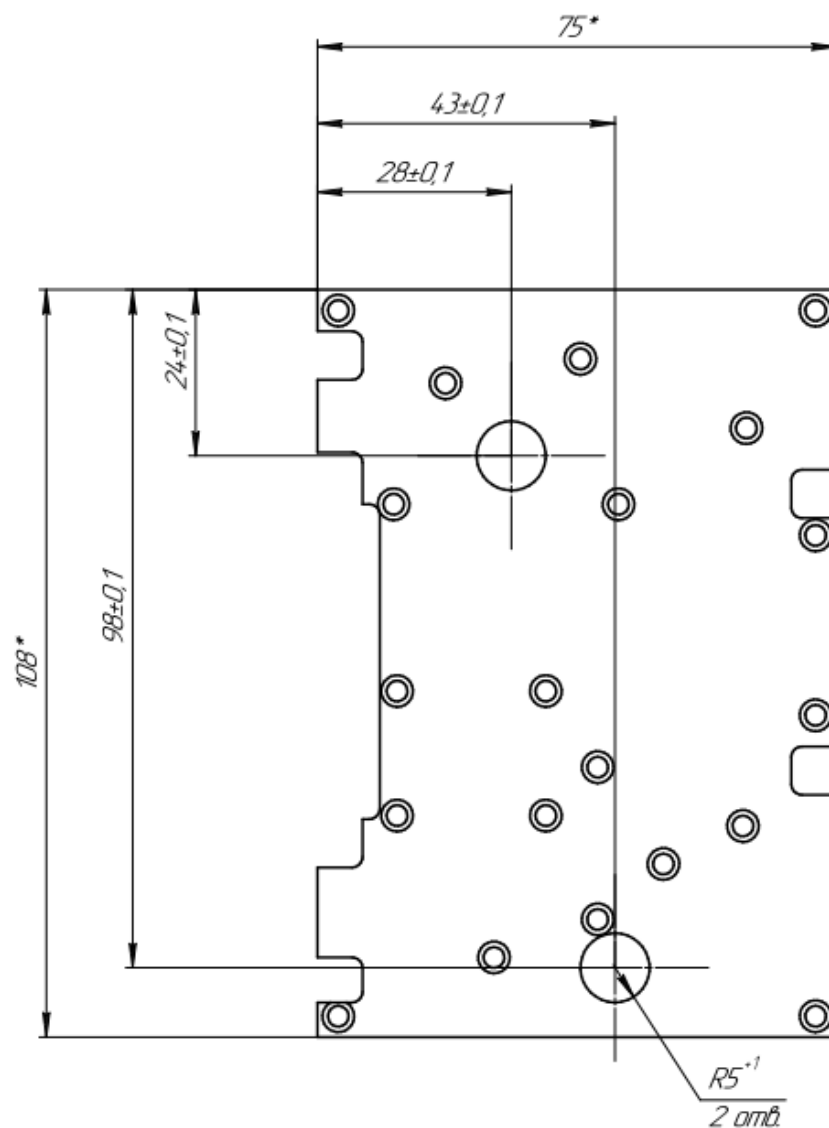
Эскиз крышки ЖНКЮ.741424.703 с отверстиями для настройки фильтров
